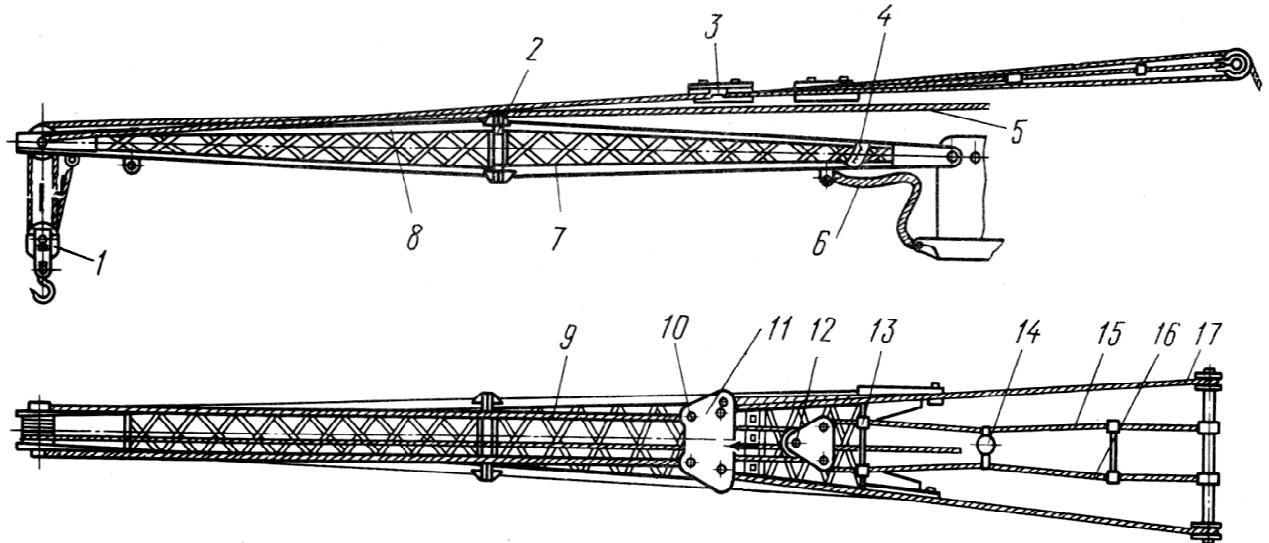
Стреловое оборудование кранов КС-3561: 1 – крюковая подвеска, 2 – стрела, 3 – полиспаст подъёма стрелы, 4 – указатель вылетов, 5, 17 – грузовой и стреловой канаты, 6 – предохранительное устройство, 7 – основание стрелы, 8 – головка стрелы, 9, 13, 15, 16 – растяжки, 10, 18 – оси, 11, 12 – траверсы, 14 – датчик усилий ограничителя грузоподъёмности, 19 – блоки
